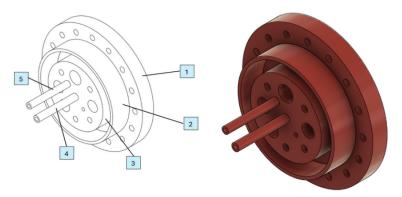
Vista isométrica representativa de prototipo de molde universal.
